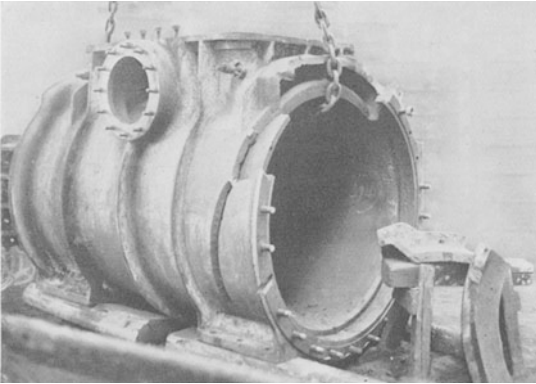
Dampfzylinder, zur Schweißung vorbereitet.
